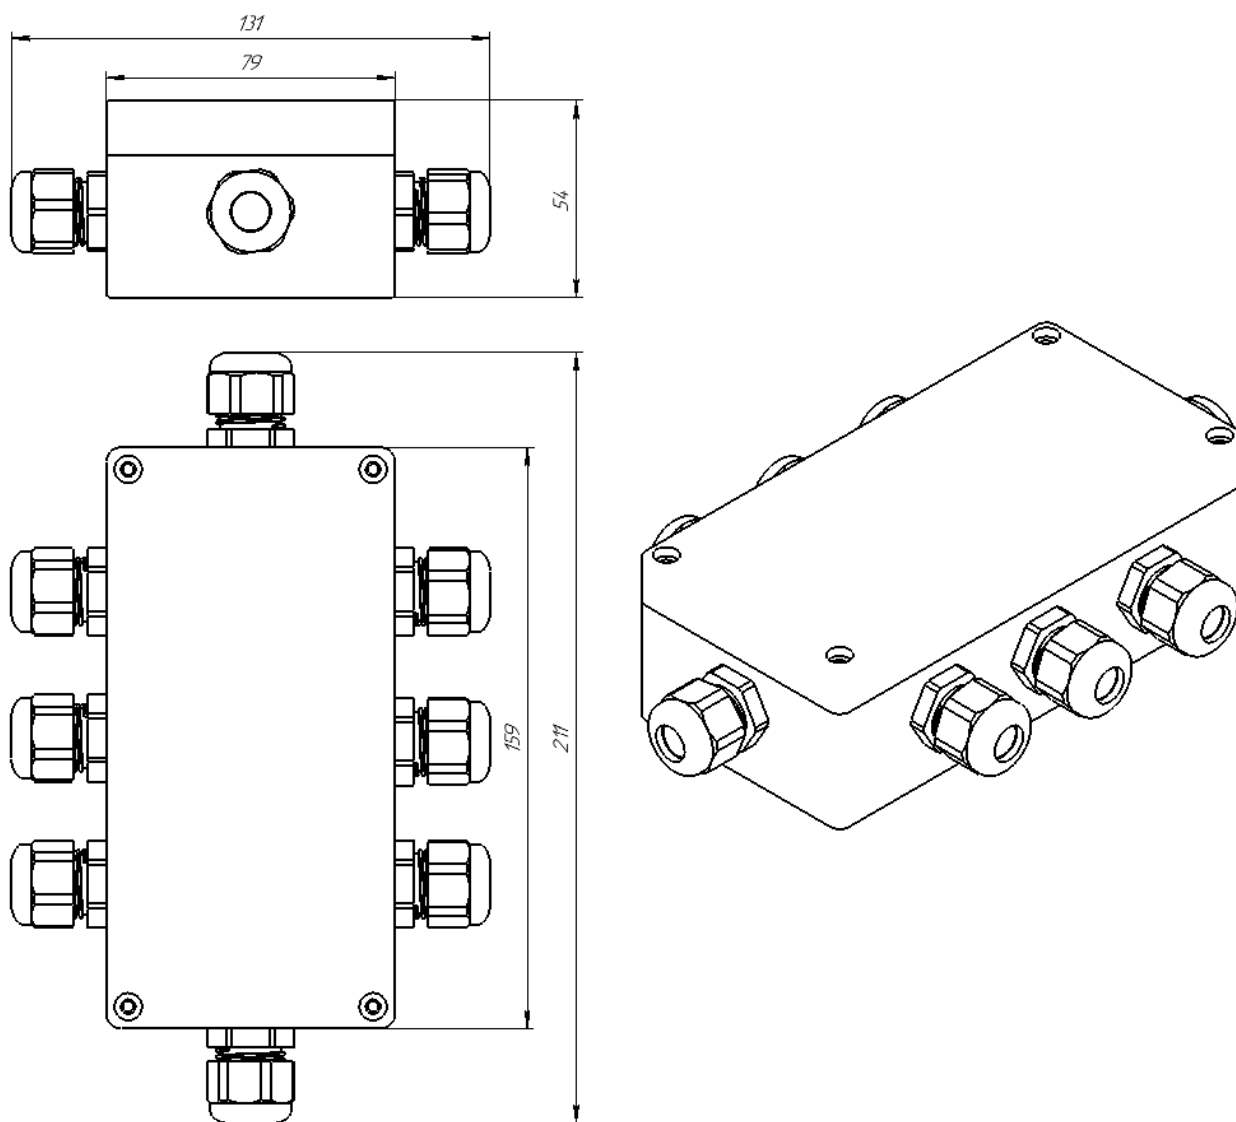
Габаритные и установочные размеры ПР-8У IP65
